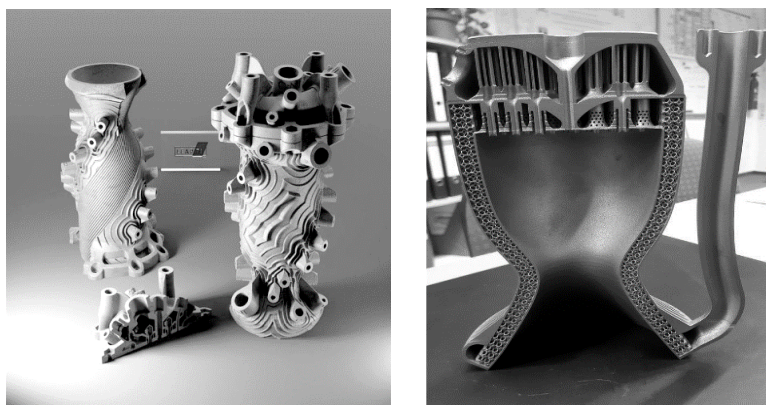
Ракетные двигатели, полученные способом 3D печати металлом
